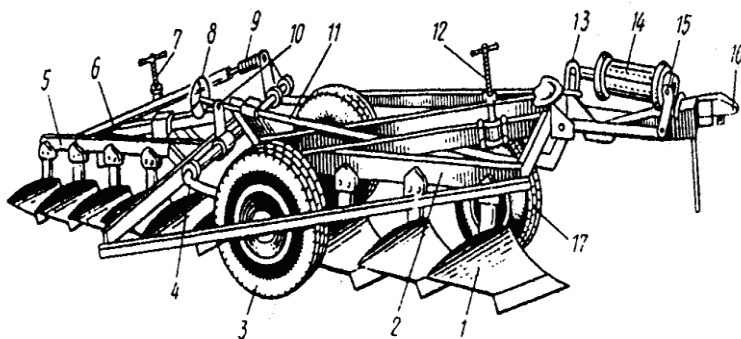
Лемешный плуг-лушительник ППЛ-10-25: 1 – корпус; 2, 5 – секция рамы; 3, 17 – колеса; 4 – ось; 6 – штанга; 7, 12 – регуляторы глубины; 8 – штурвал; 9 – догрузатель; 10 – кронштейн; 11 – тяга; 13 – рычаг; 14 – гидроцилиндр; 15 – поводок; 16 – прицепное устройство
